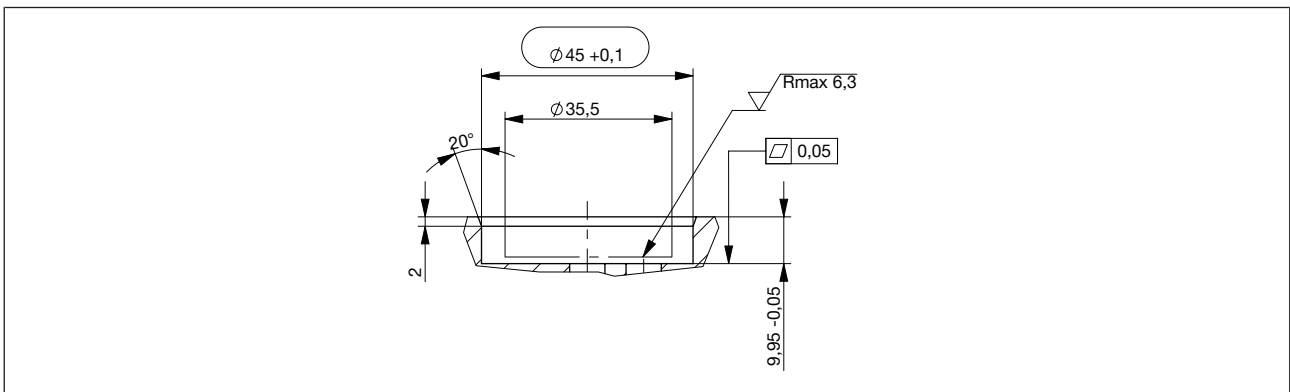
Anschlussbild 1 Einsteckflansch-Variante FC23
